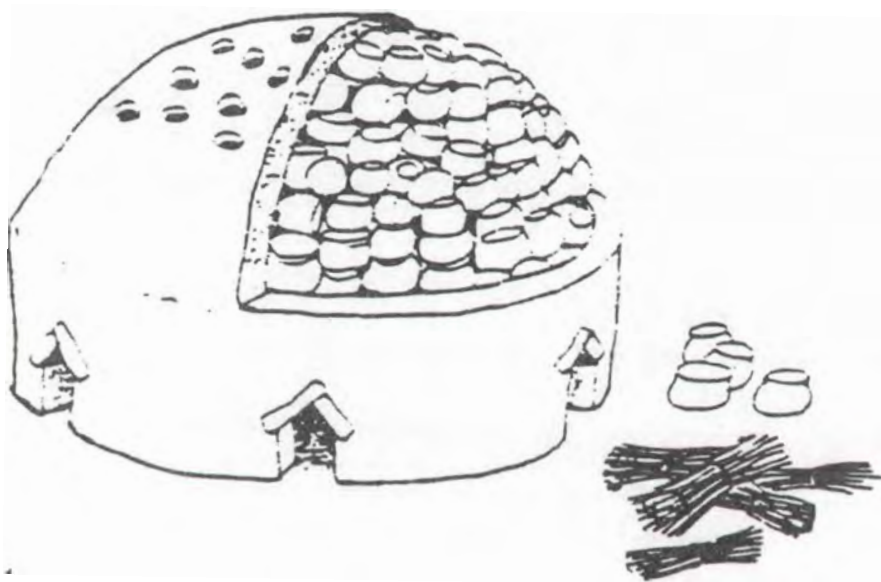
Horno de muro circular bajo con aberturas para el fuego
